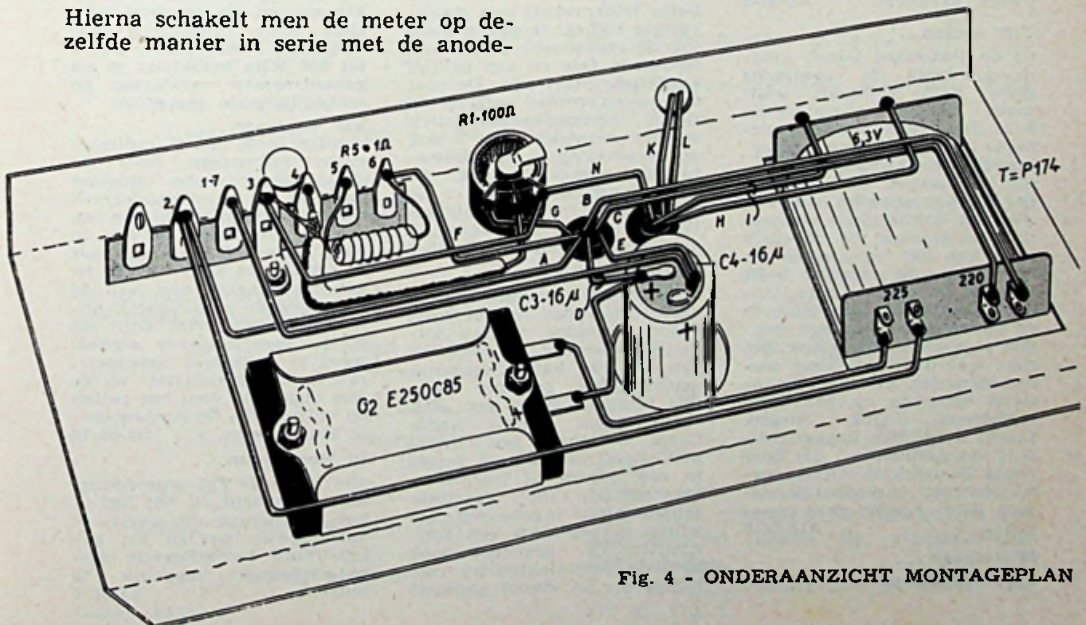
ONDERAANZICHT MONTAGEPLAN
